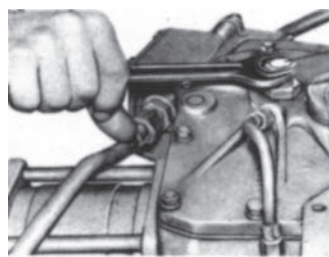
Регулировка вертикального перемещения поворотного вала.
